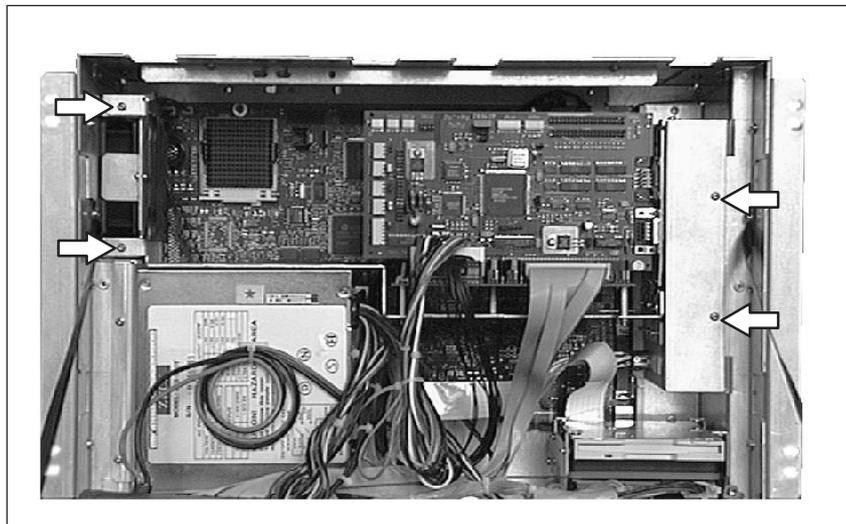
Befestigung des Querträgers am Systemgehäuse
